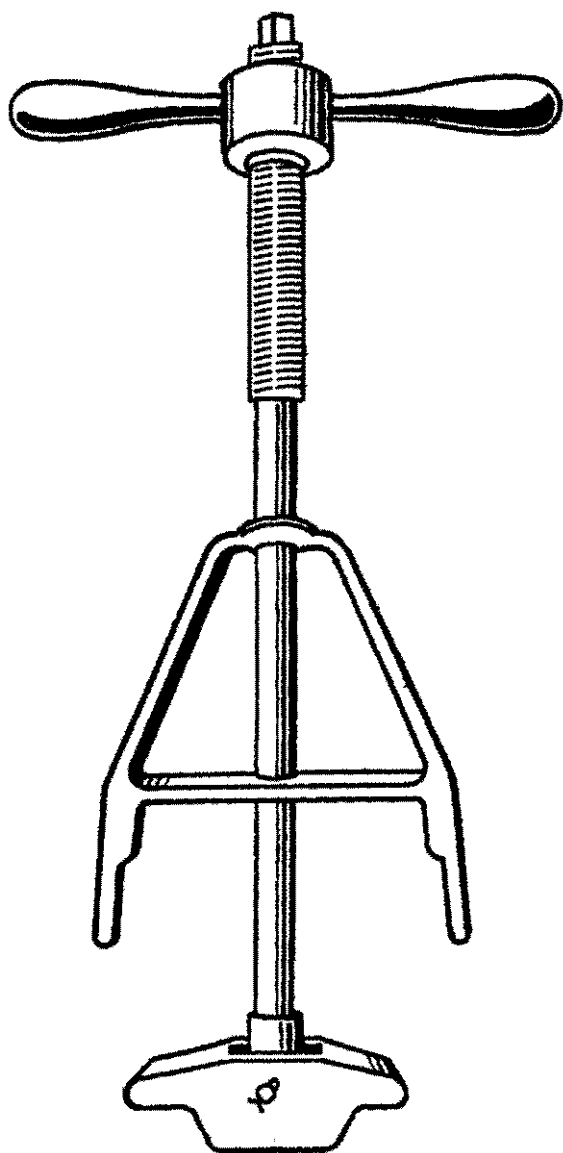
Съемник для выпрессовки гильз из блока цилиндров
